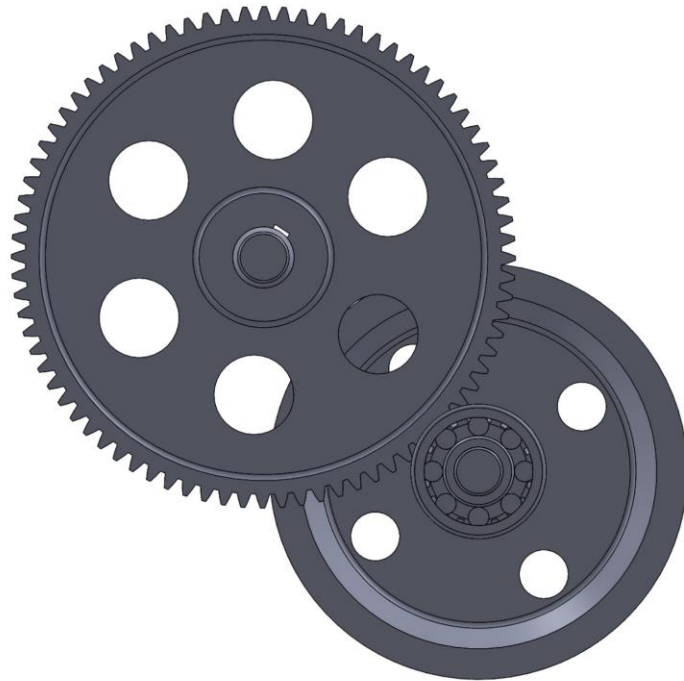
Конструкція вал-шестерня вигляд спереду
